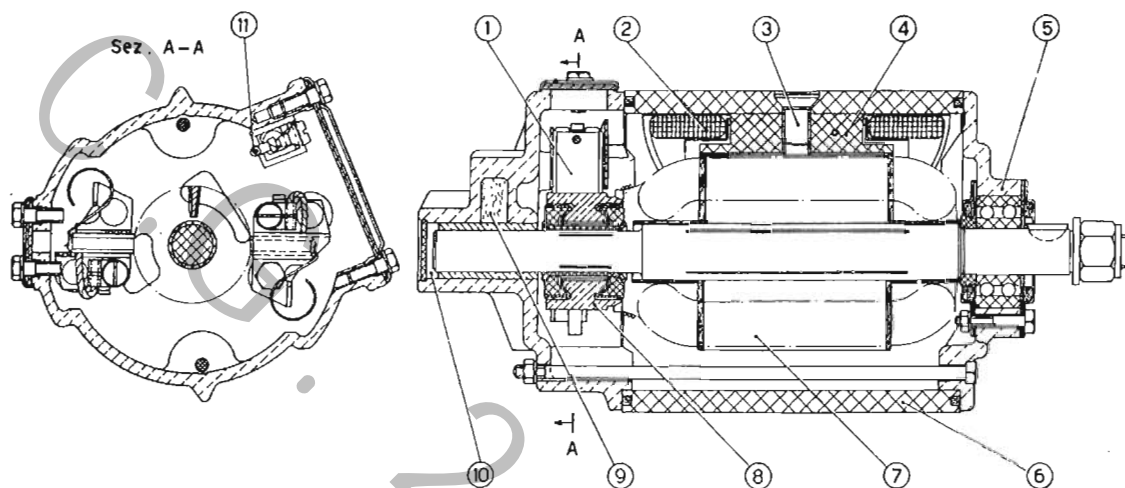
Sezione longitudinale e trasversale della dinamo tipo R 115-140/24 - 1600 Var. 2.
